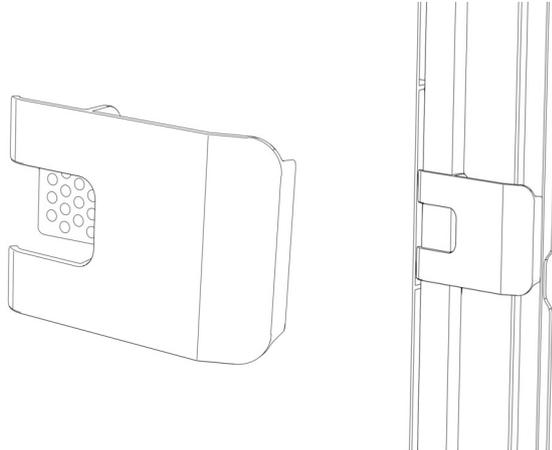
Schlauchklammer (links); Schlauchklammer installiert (rechts)
